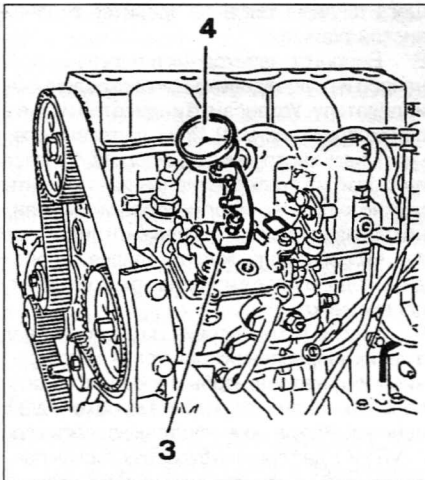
Стрелочный индикатор для регулировки опережения впрыска топливного насоса высокого давления (4) и соответствующий опорный кронштейн (3), закрепленные на топливном насосе высокого давления
